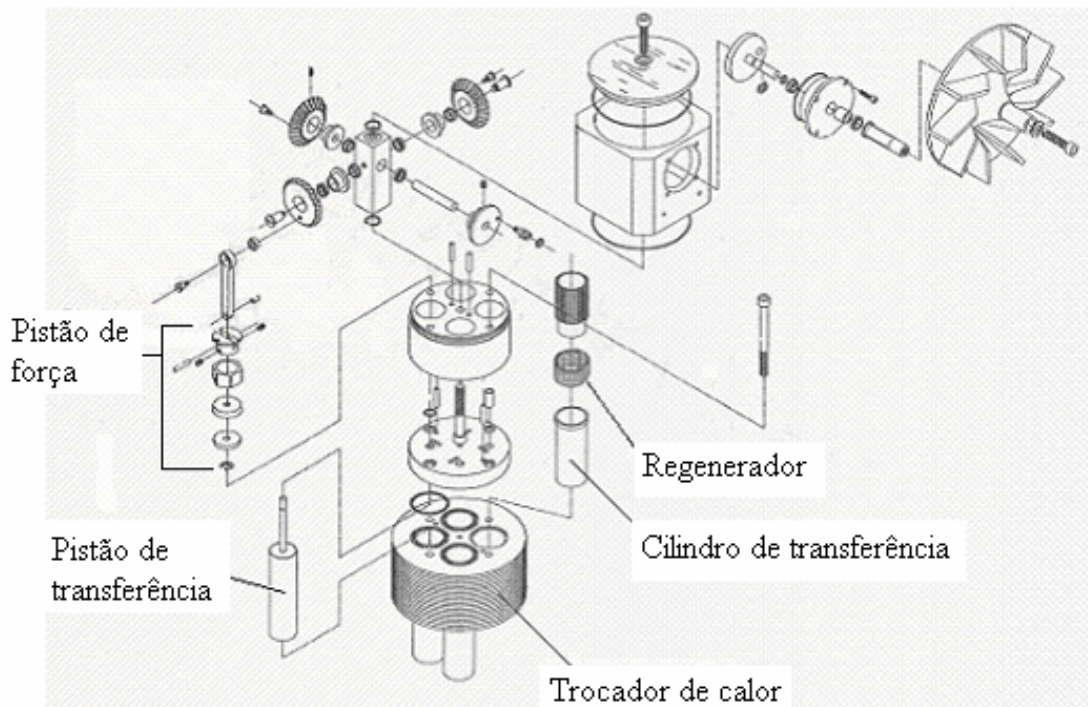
Vista explodida do motor Stirling referência de projeto (STEELE, 1994)
